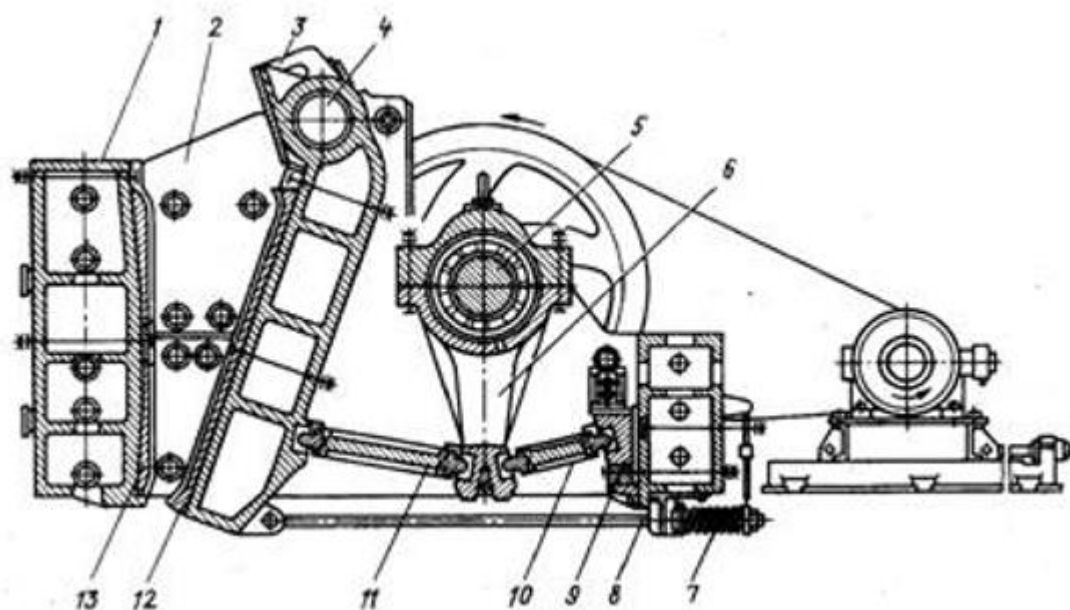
Конструкция щековой дробилки с простым движением щеки
